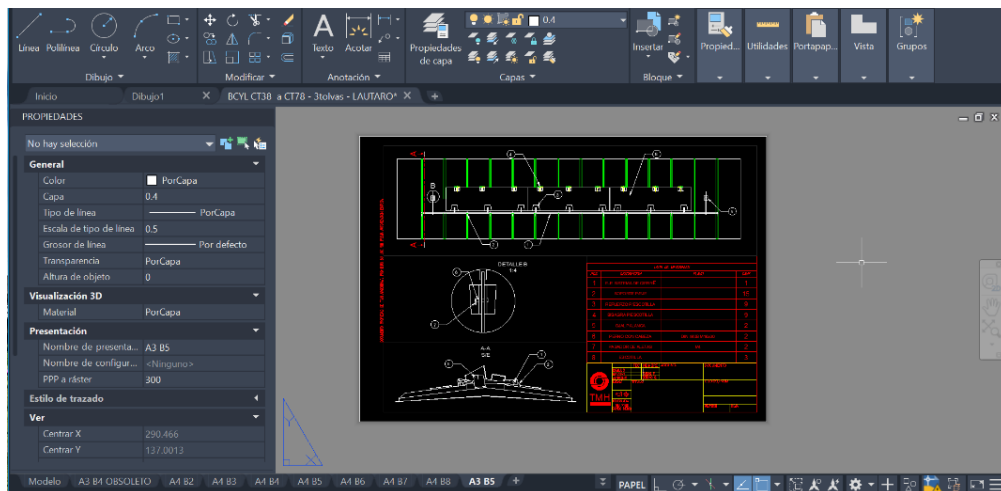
Elaboración de plano para el conjunto de sistema de carga.
